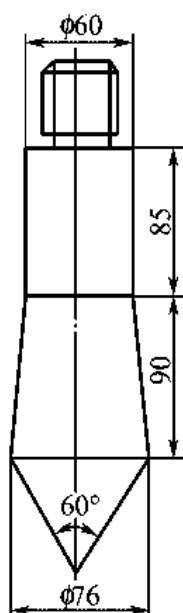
重型、超重型动力触探探头(单位:mm)
